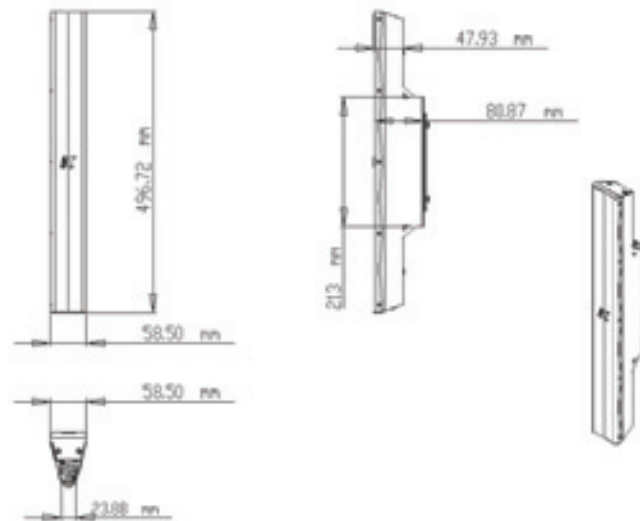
Detalles de alzado, planta y sección del altavoz, además de vista en perspectiva 3D
